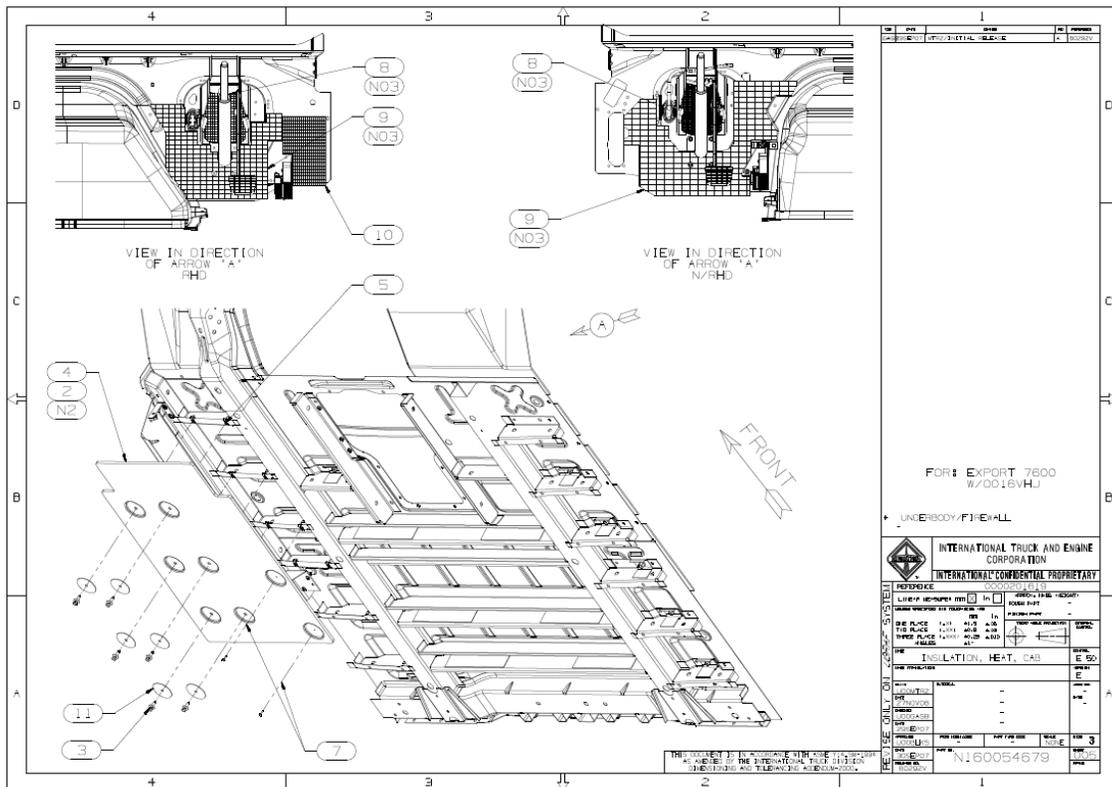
Diseño de Autocad del aislante térmico en pared de fuego
